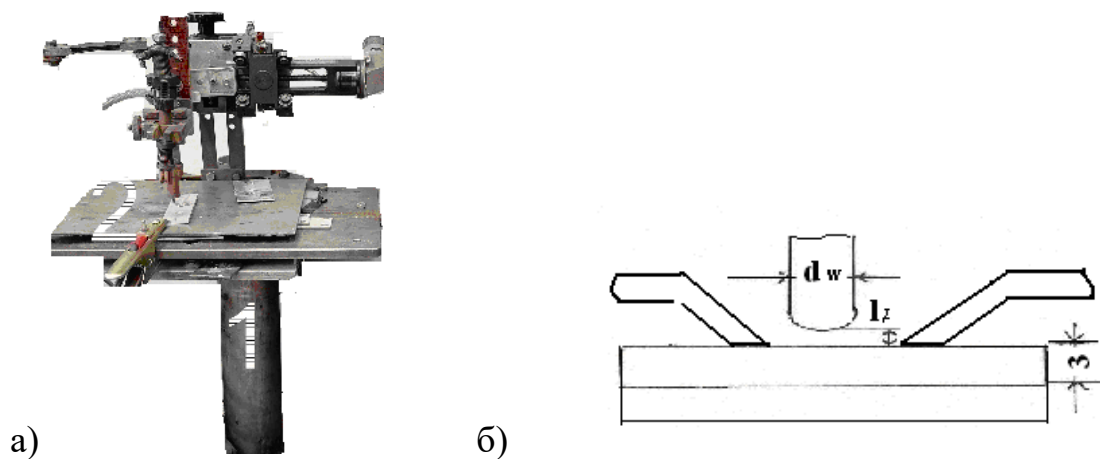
Внешний вид лабораторного стенда и схема установки прижимов
